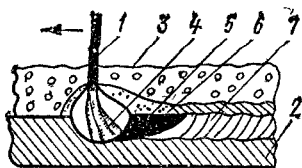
Автоматическая сварка под флюсом
